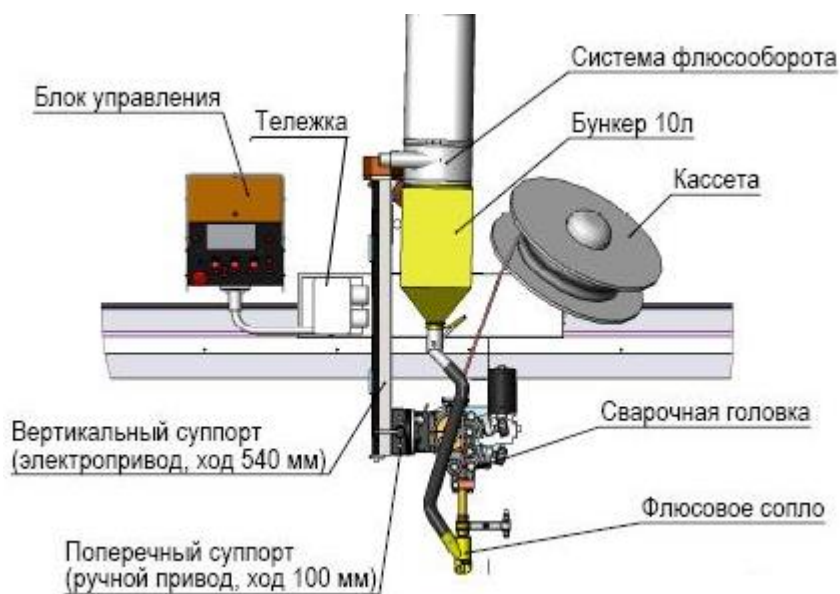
Конструкция самоходного сварочного автомата
